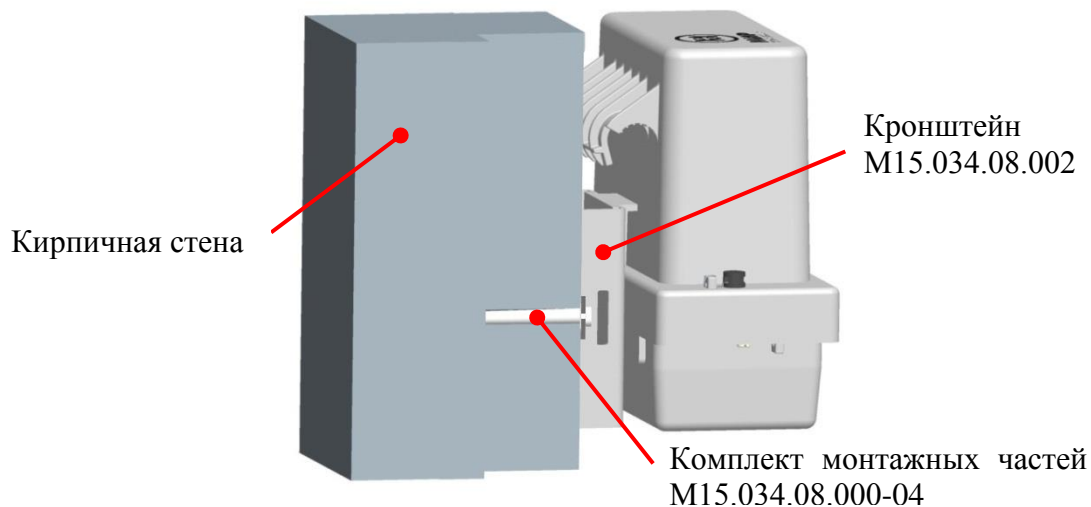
Установка счетчика на кирпичную или бетонную стену здания
